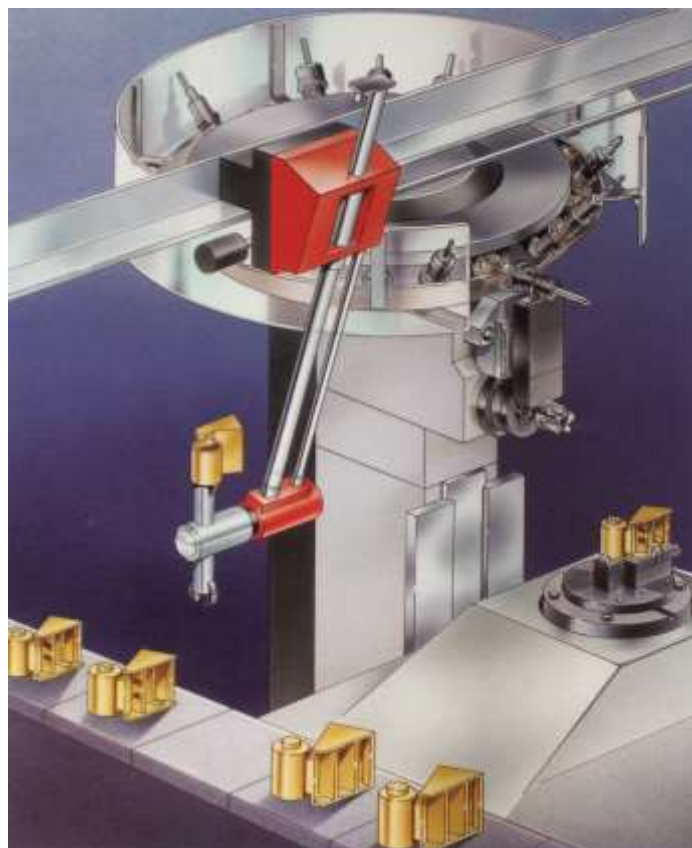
Корончатий інструментальний магазин (показано також зміну заготовок)
